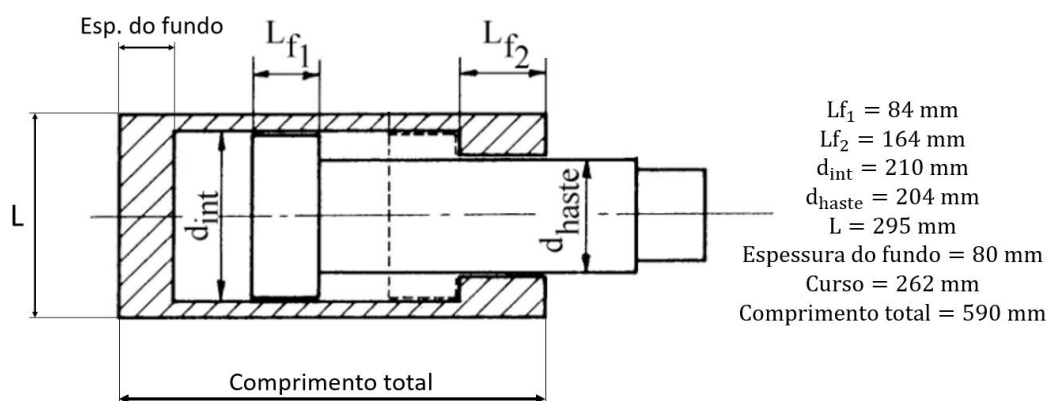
Identificação das medidas dimensionadas do cilindro hidráulico projetado (adaptado de [67]).
